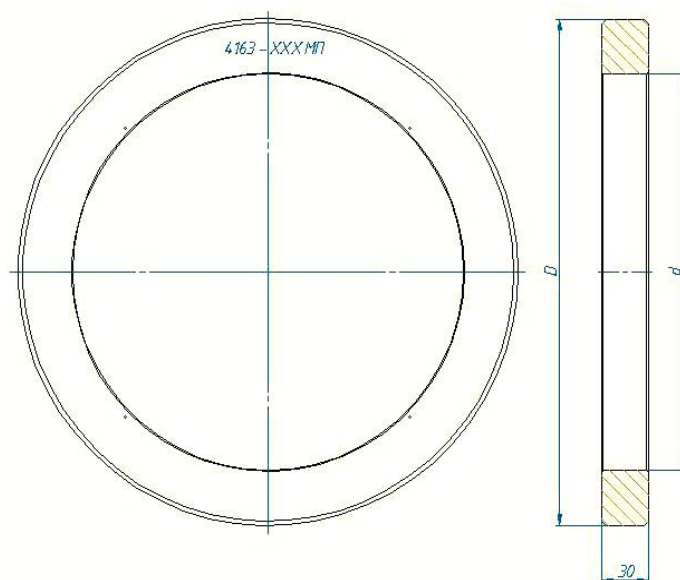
Эскиз установочных мер для приборов модели 4163 с обозначением основных размеров
